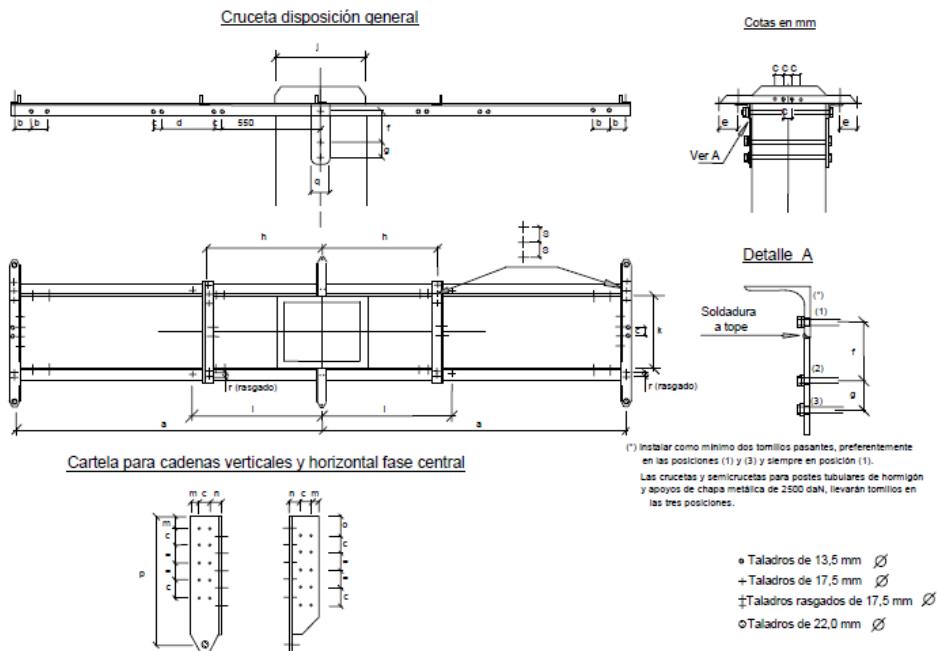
Crucetas para apoyos de hormigón y chapa metálica
